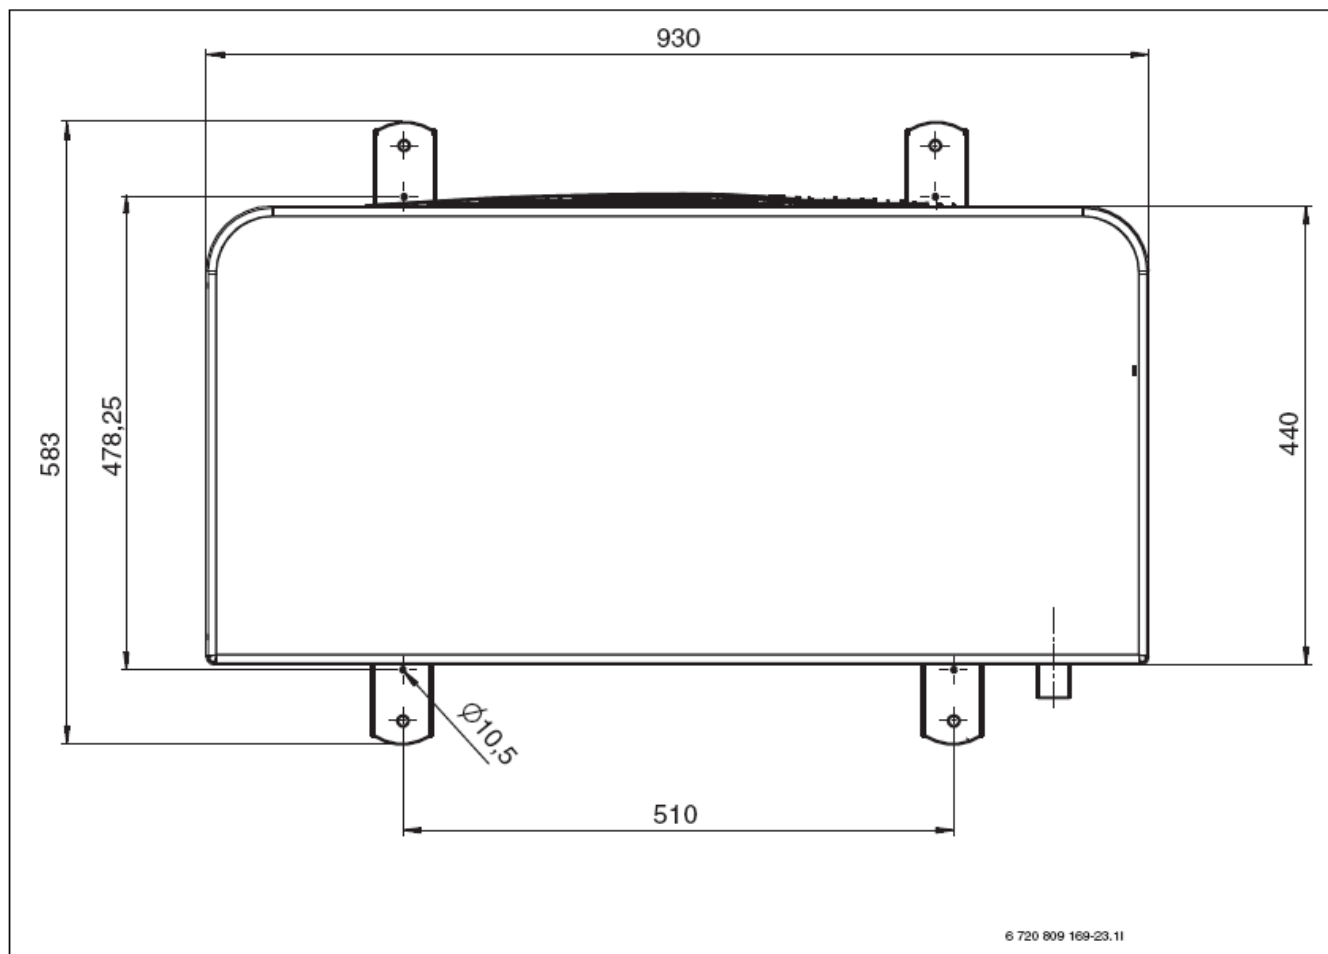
Габаритные размеры наружного блока 7/9, вид сверху
